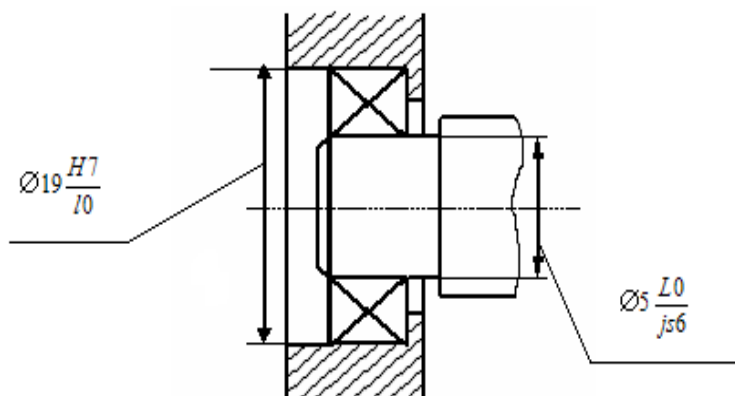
Обозначение посадок подшипникового узла на чертеже
